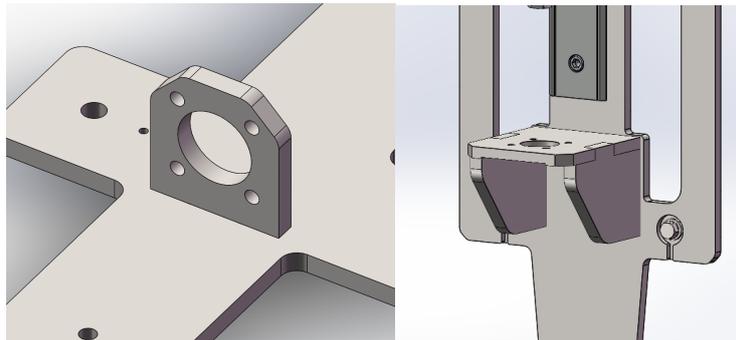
y 29. Primera (izquierda) y segunda versión (derecha) del soporte principal del elevador
